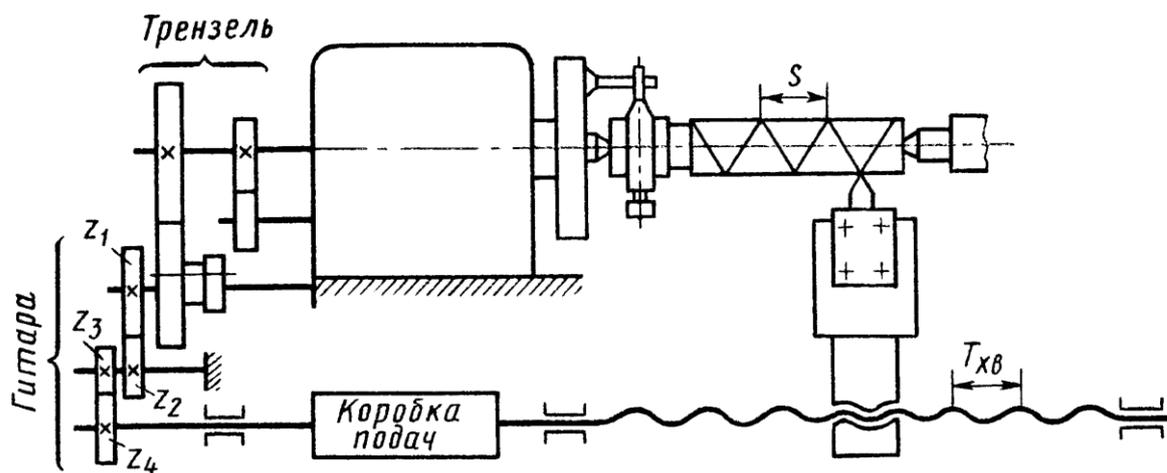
Схема нарезания резьбы на токарно-винтовом станке
